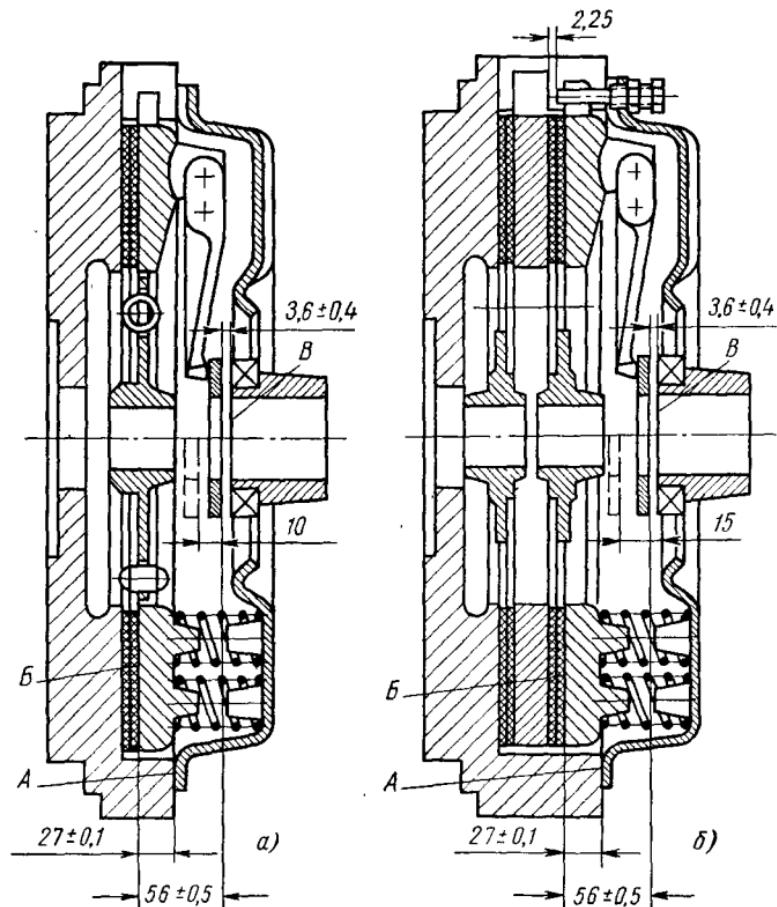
Схема регулировочных и контрольных размеров сцеплений:
